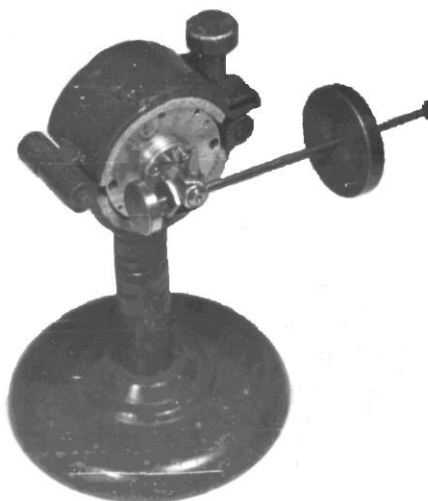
Приспособление для проверки крутящего момента и определения жесткости магнитной пружины ЭМП
